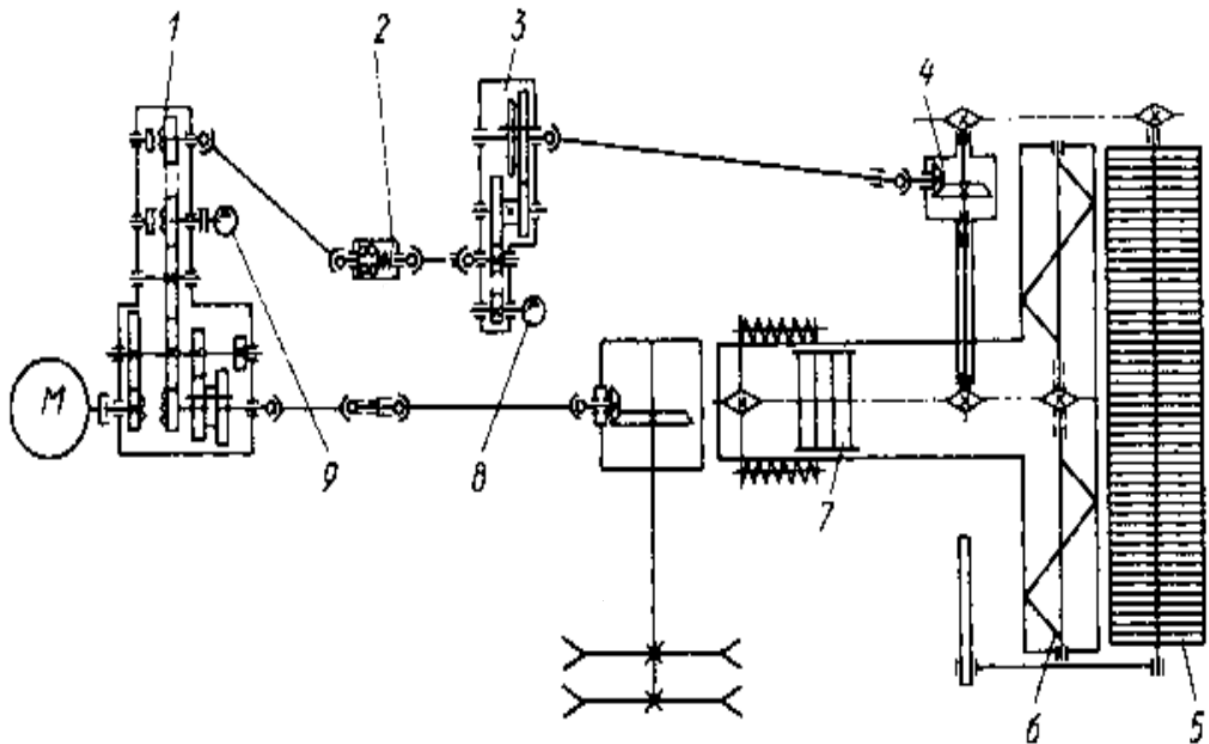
Кинематическая схема подметально-уборочной машины:
